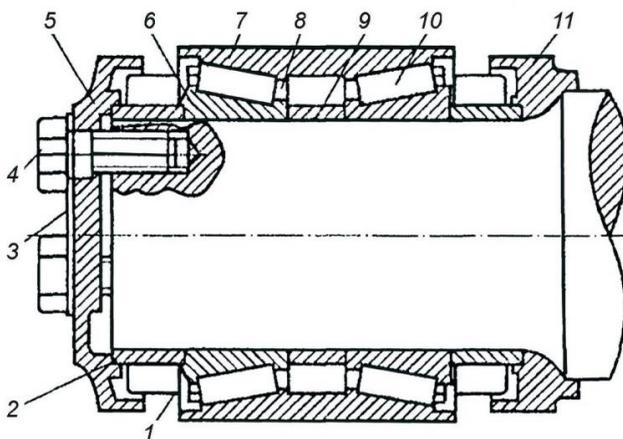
Буксовый узел с коническими роликовыми подшипниками
